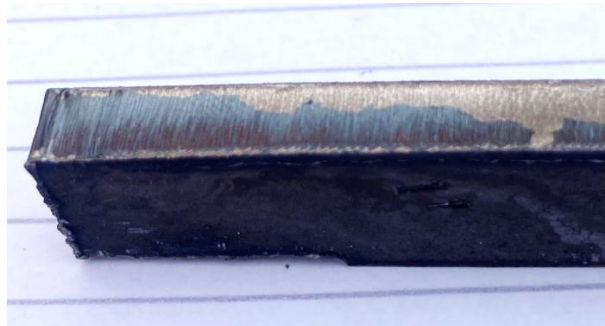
Příprava zkušebních těles (laboratoř FSI)
